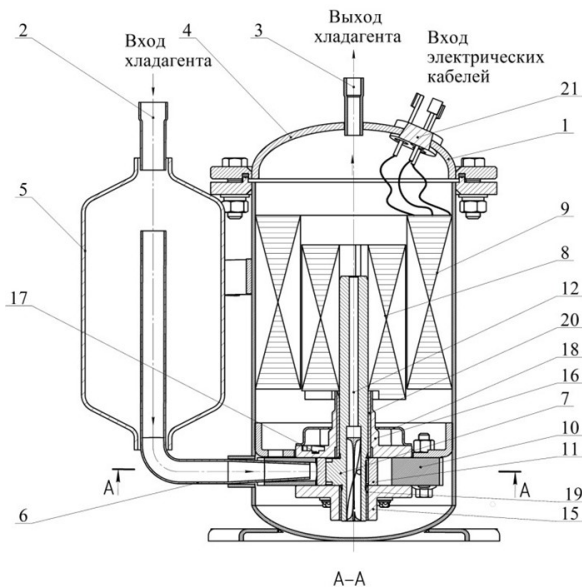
Конструкция макета ротационного компрессорного агрегата:
